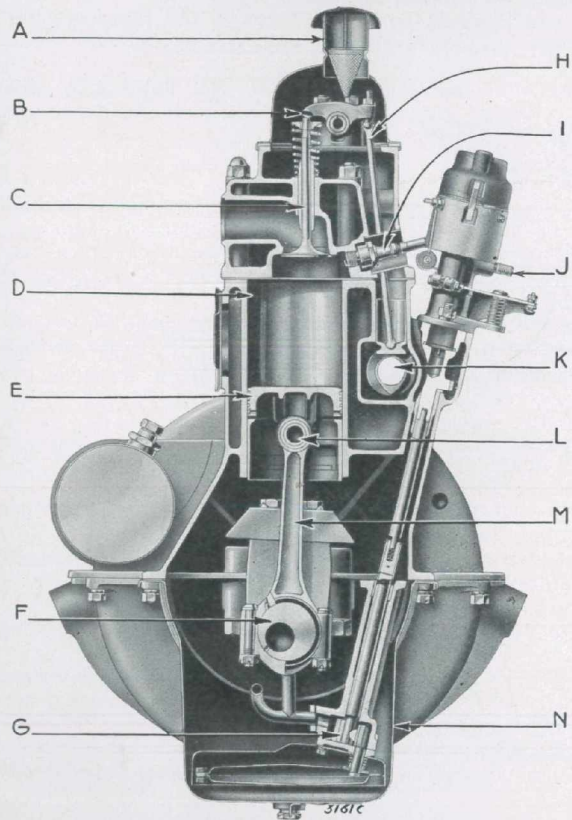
QUERSCHNITT DURCH DEN MOTOR
